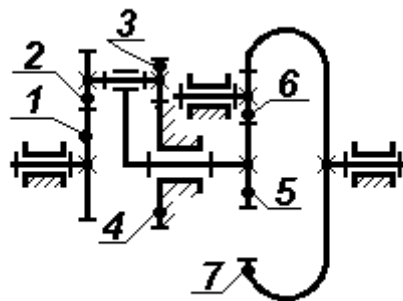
Схема комбінованого багатоланкового зубчастого механізму
